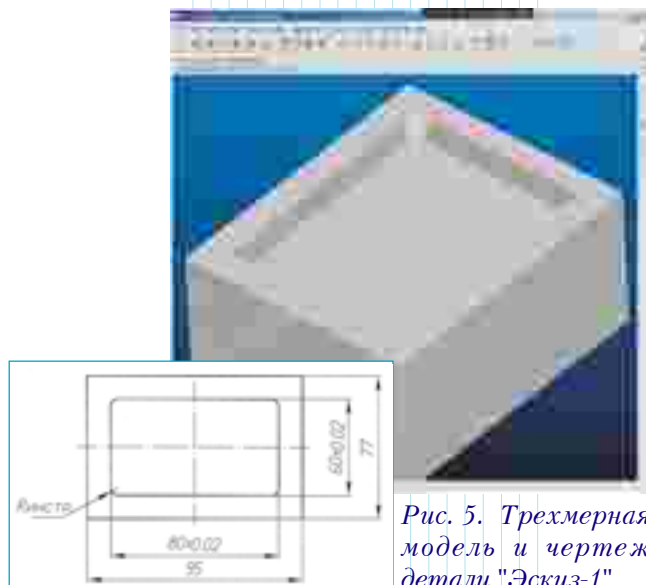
Трехмерная модель и чертеж детали "Эскиз-1"
